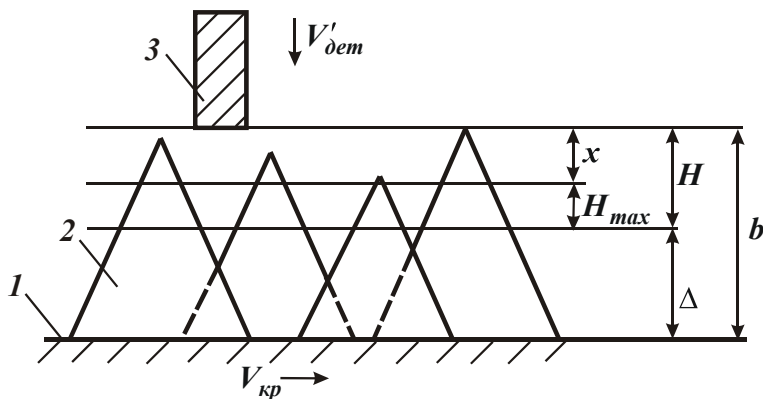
Расчетная схема параметров шлифования: 1 – связка круга; 2 – зерно; 3 – обрабатываемый образец.
